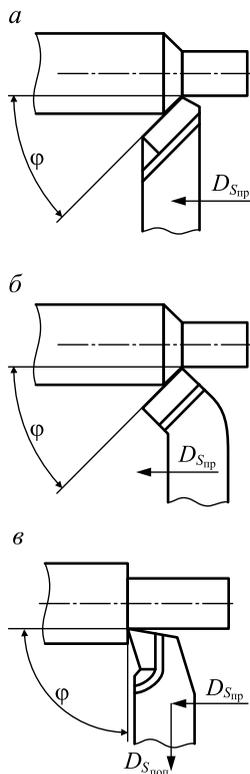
Проходные резцы: а — прямой; б — отогнутый; в — упорный
